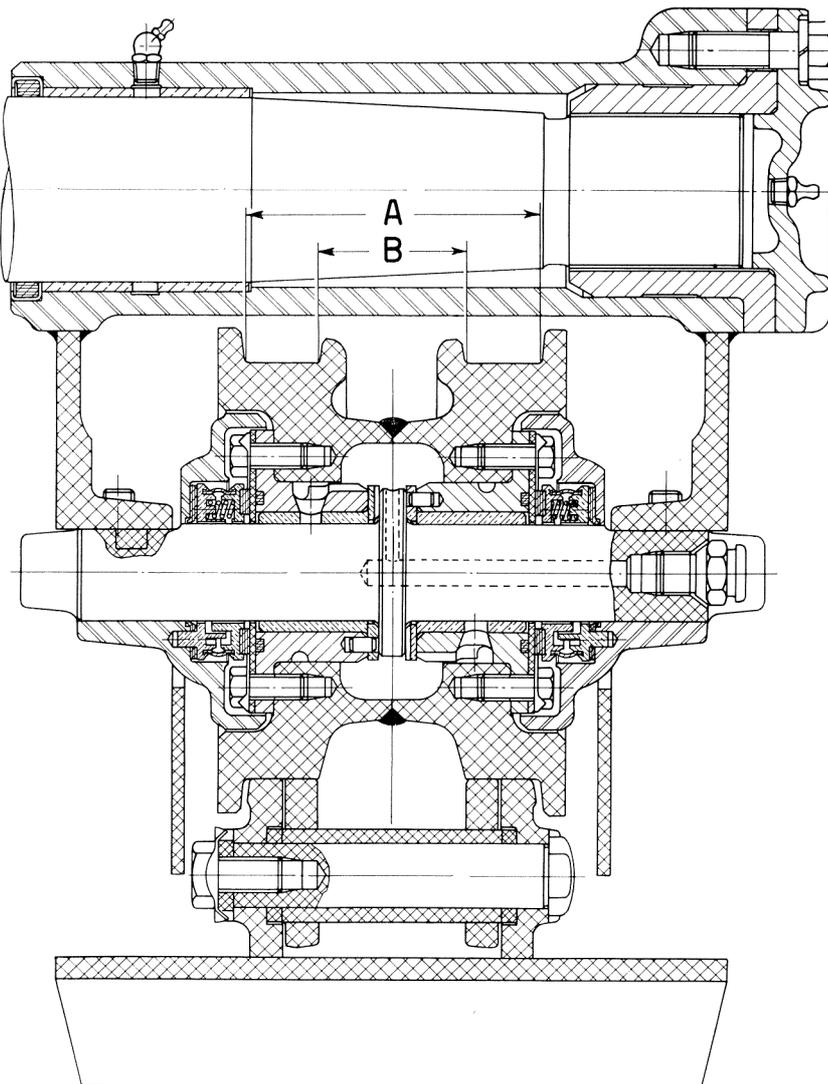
Coupe sur la barre transversale et sur un galet porteur.
